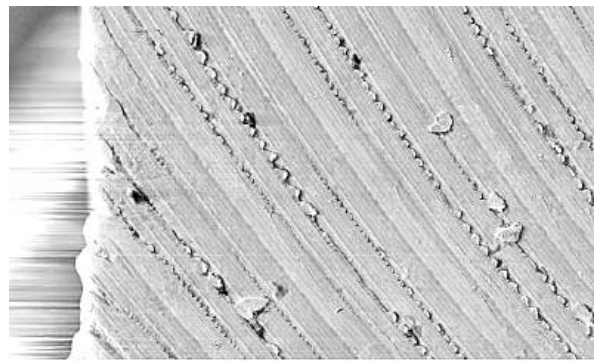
Типові частинки на поверхні деталі після фрезерування
